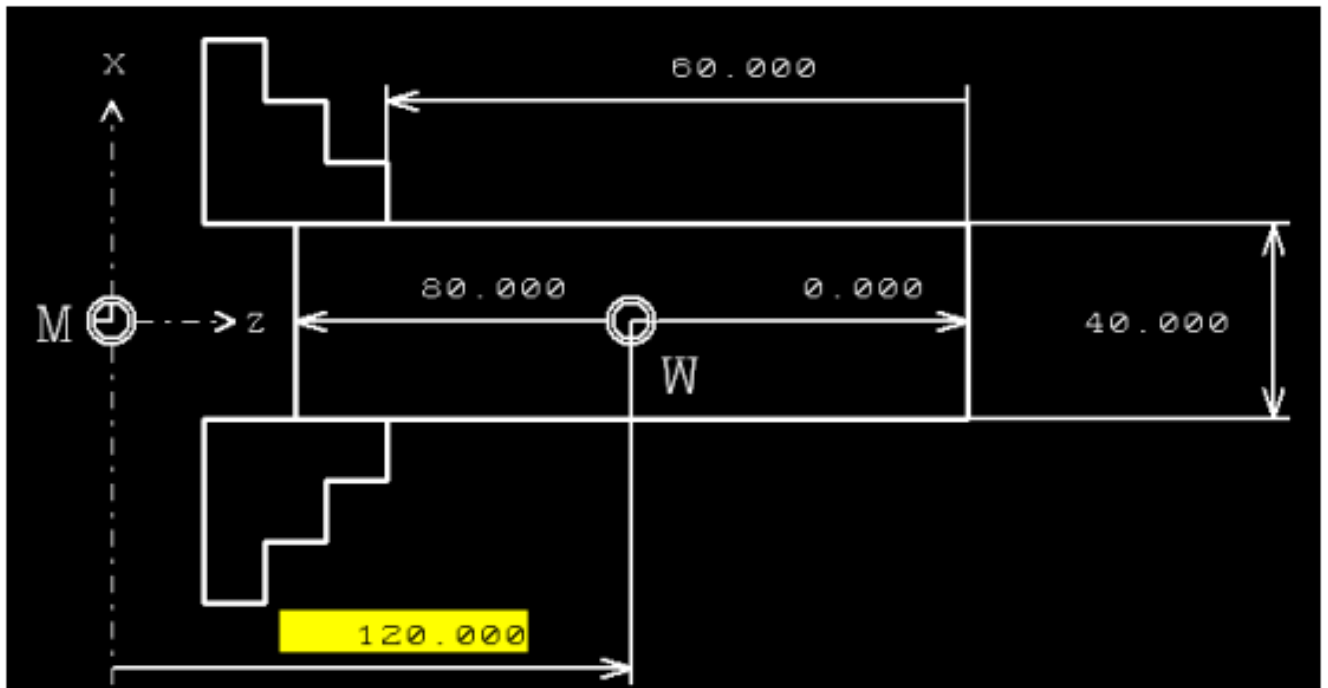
Прив'язка нуля деталі до нуля верстата
